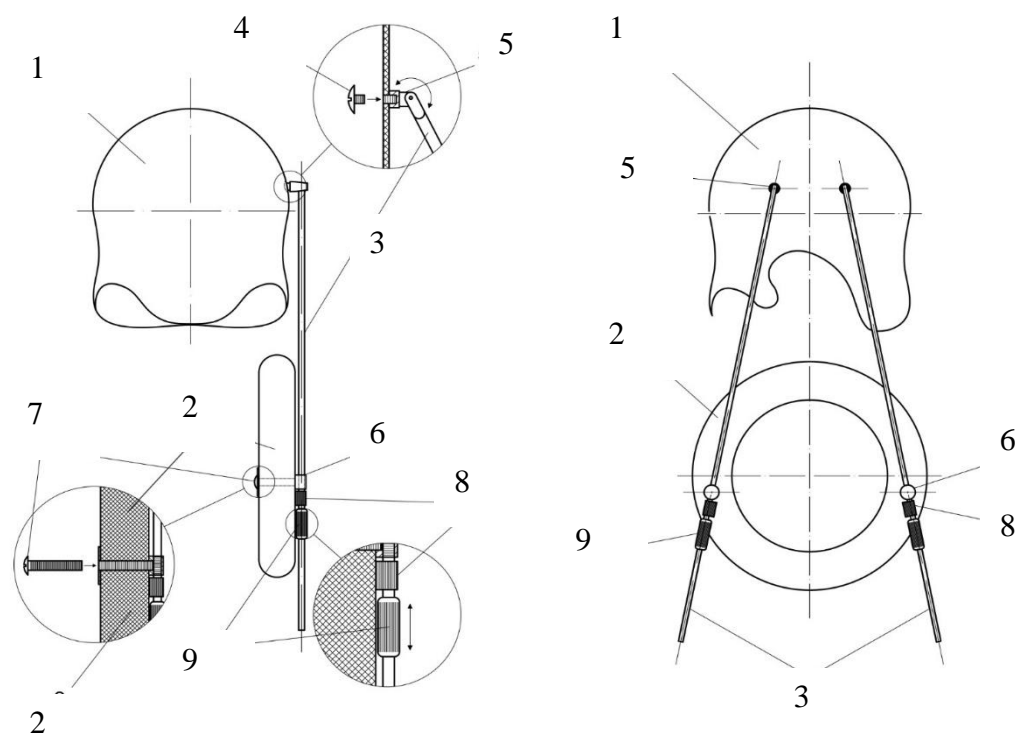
Конструкция устройства для лечения поврежденных стволов плечевого сплетения. А - вид устройства спереди; В - вид устройства сбоку. 1- шлем, 2- фиксирующее кольцо, 3- резьбовые штанги, 4 - винты, 5- кронштейны, 6- втулки, 7- винты, 8 и 9 - гайки (8 и 9).
